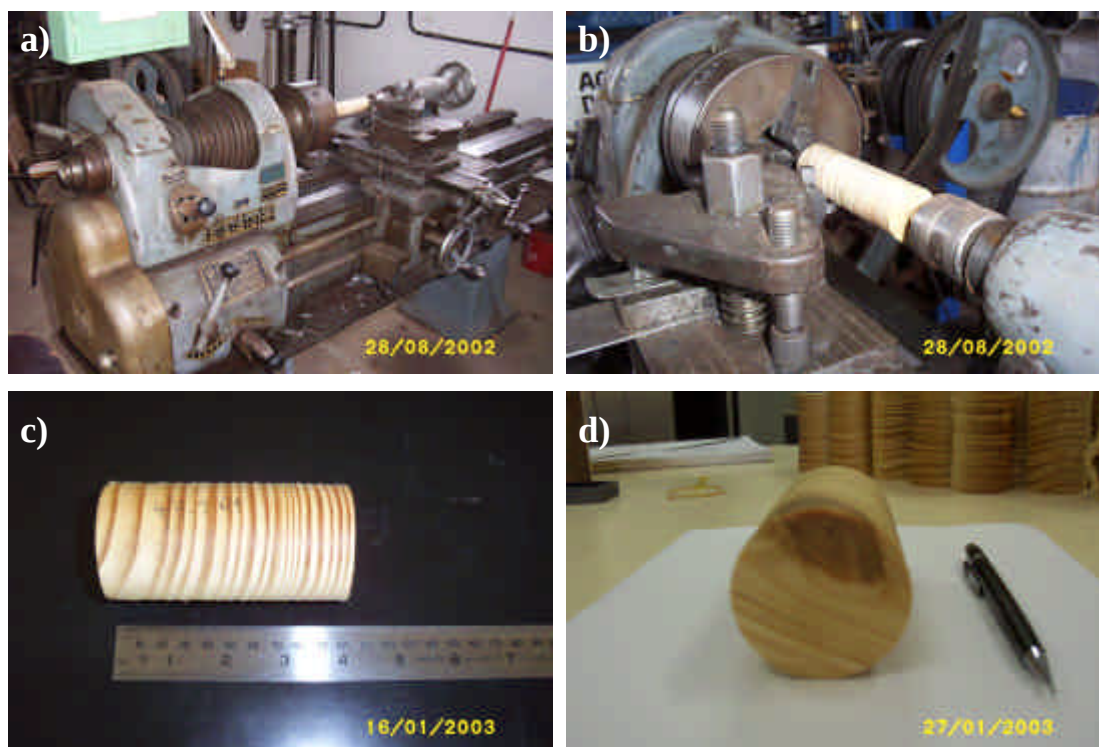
Confecção dos corpos-de-prova radiais. a) vista geral do torno; b) finalização do torneamento do corpo-de-prova; c) corpo-de-prova isento de defeito e d) corpo-de-prova com defeito.
